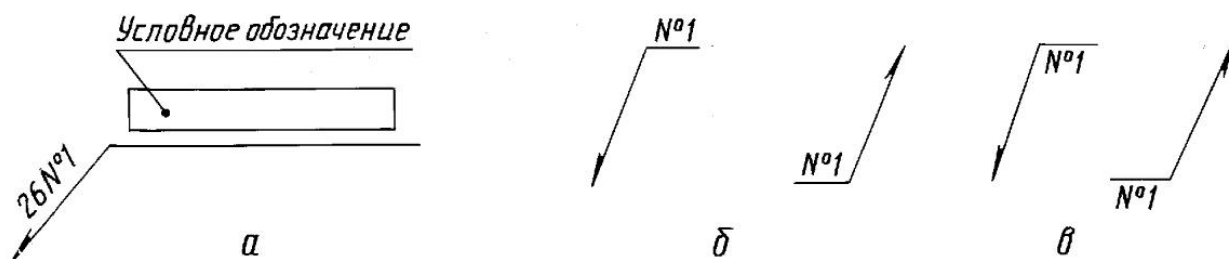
Обозначения одинаковых сварных швов
